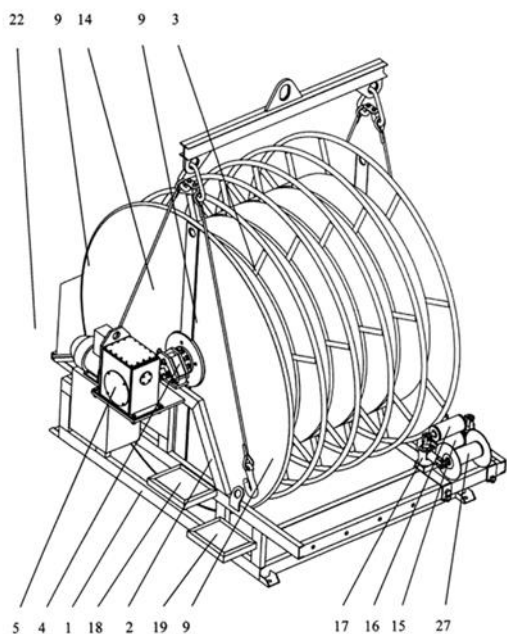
Установка для сворачивания и разворачивания гибкого плоскосворачиваемого рукава (вид установки в аксонометрии с левой стороны):
